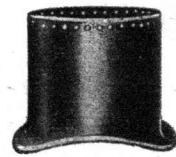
Dampfdom, nach dem Umbördeln geschnitten.
